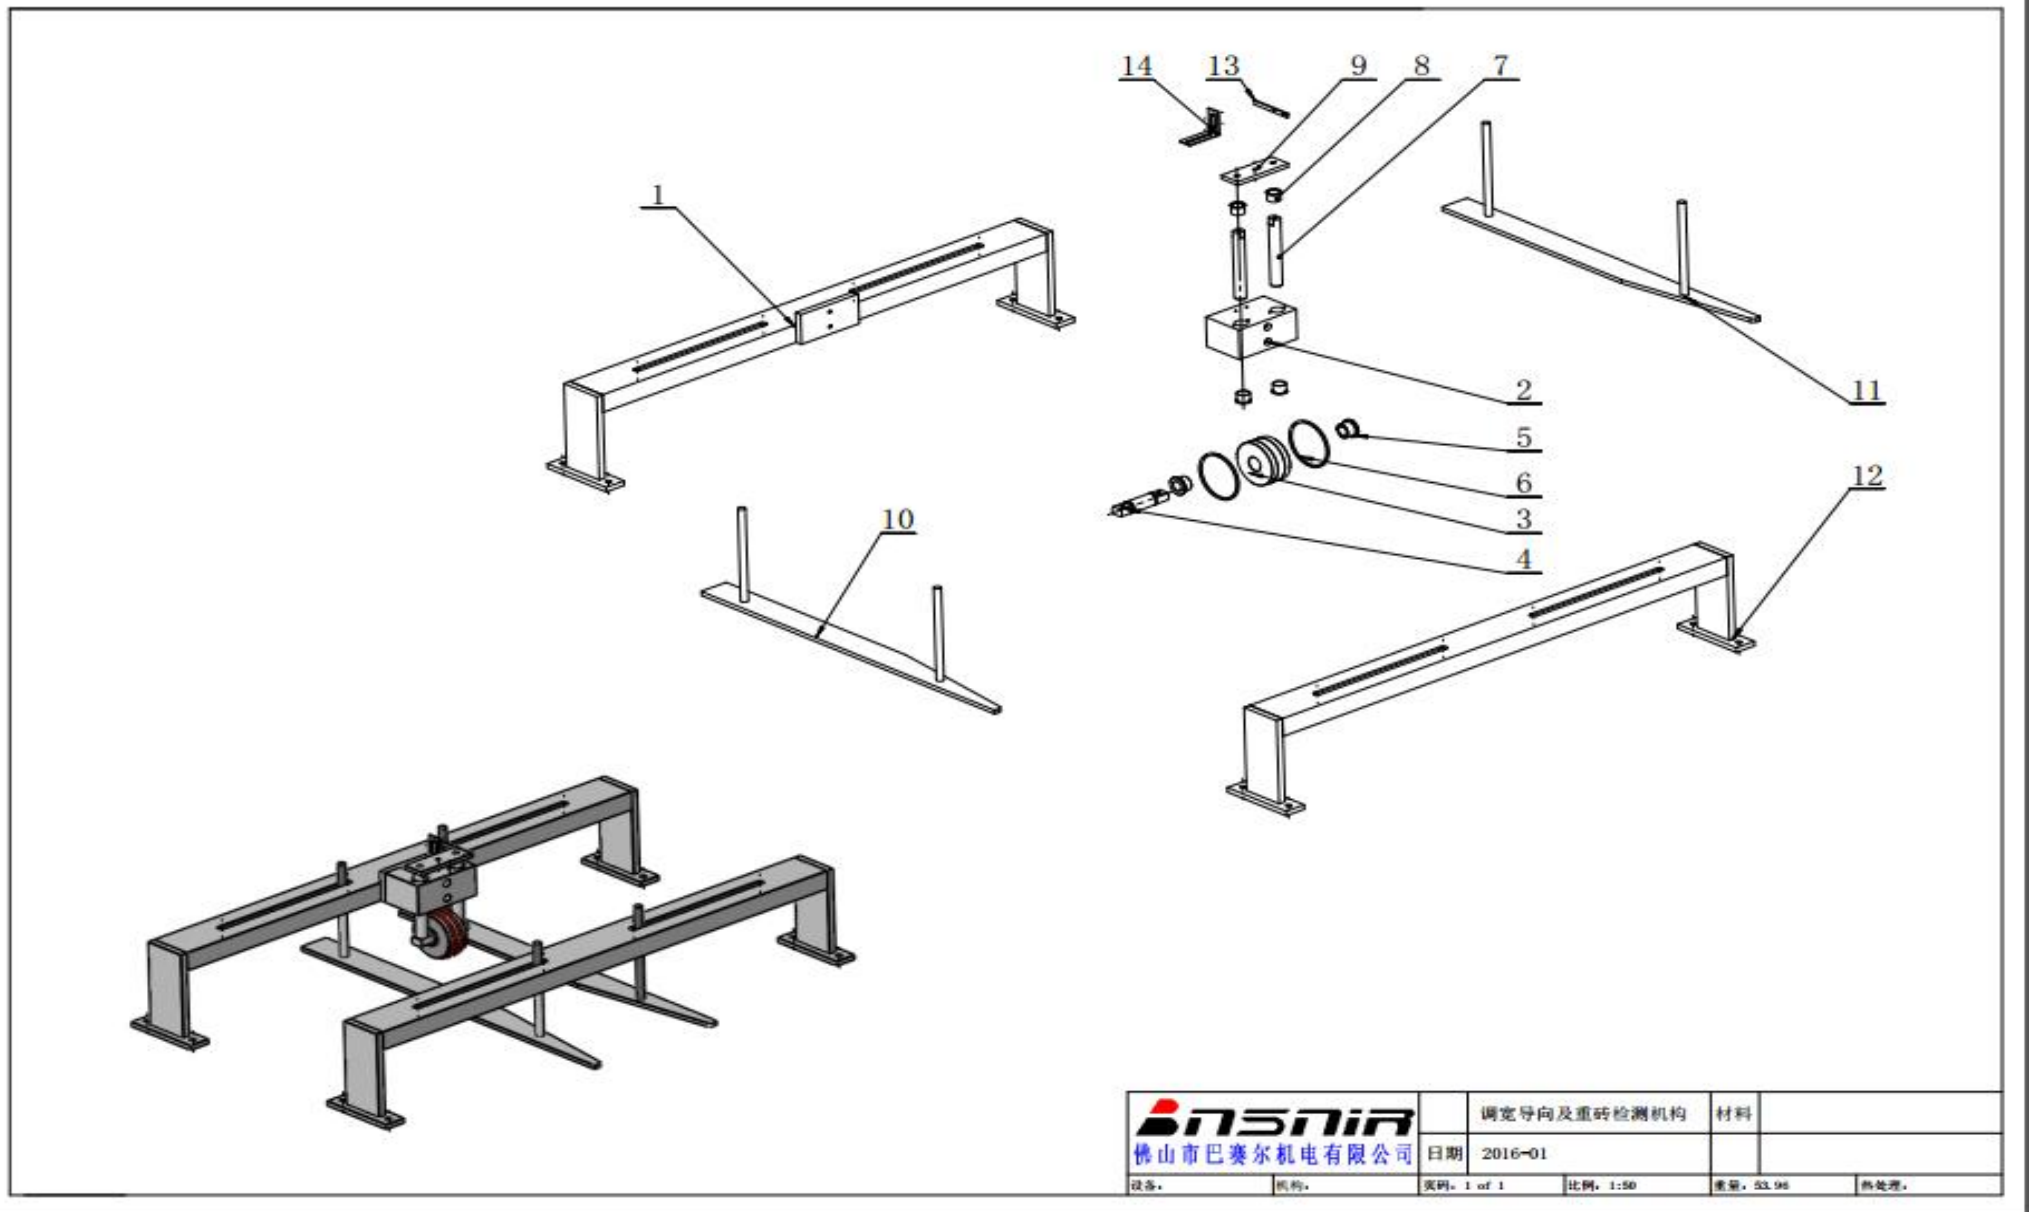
1 机架部分——调宽导向及重砖检测机构装配图 picture2-1 Rack part -- Assembly drawing of width adjustment guide and heavy brick detection mechanism
